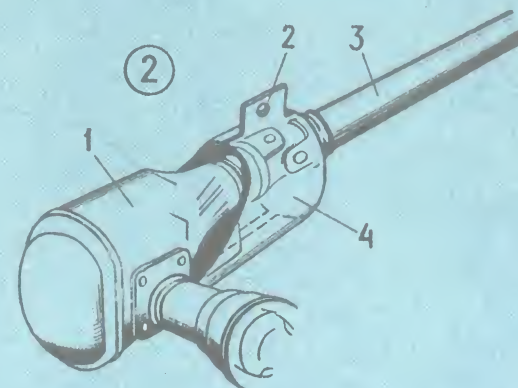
Установка защитного кожуха: 1 — картер редуктора переднего моста; 2 — отверстие для болта, крепящего рабочий цилиндр в приводе сцепления; 3 — передний карданный вал; 4 — защитный кожух.
